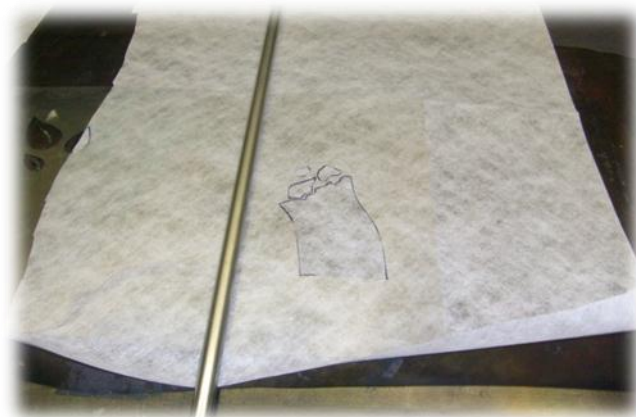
Molde e não tecido sobre a mesa de estampagem.
